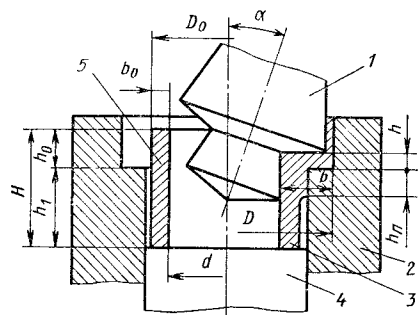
Схема формирования наружного прямоугольного бурта коническим валком:
